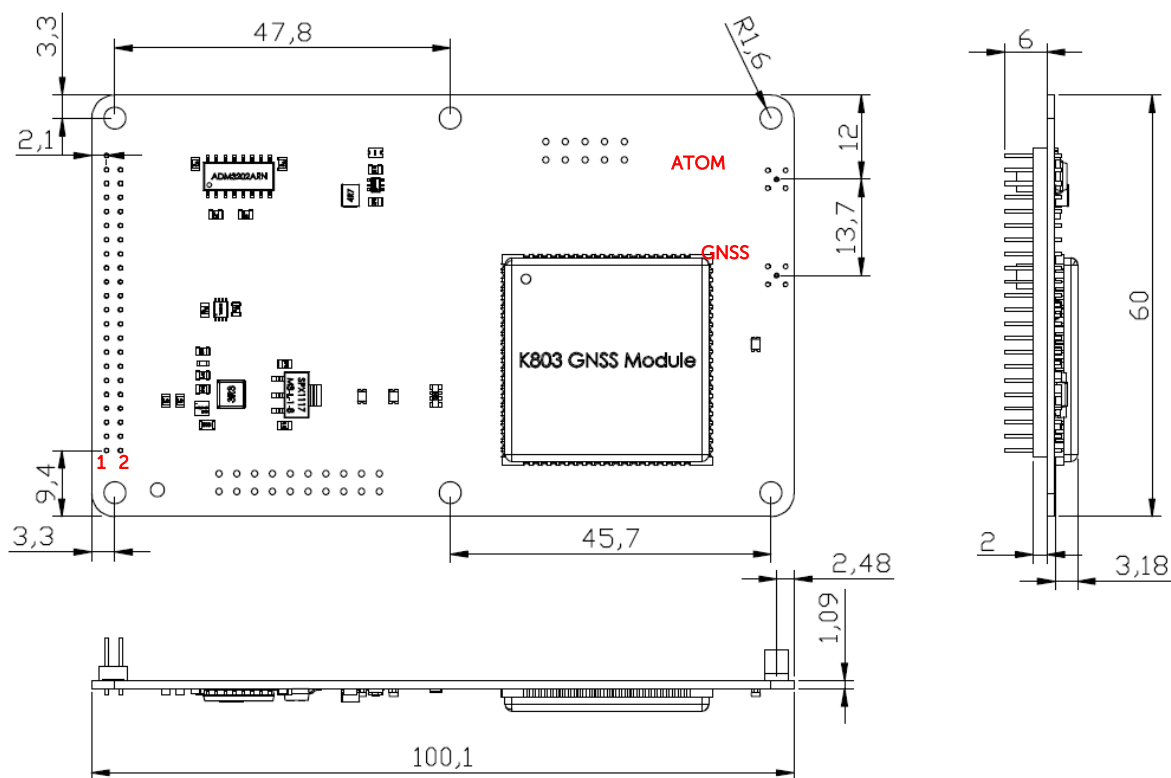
Размеры ГНСС-приемников 4GNSS типоразмера S60100 NP1/NP2/NP3/NP3I
